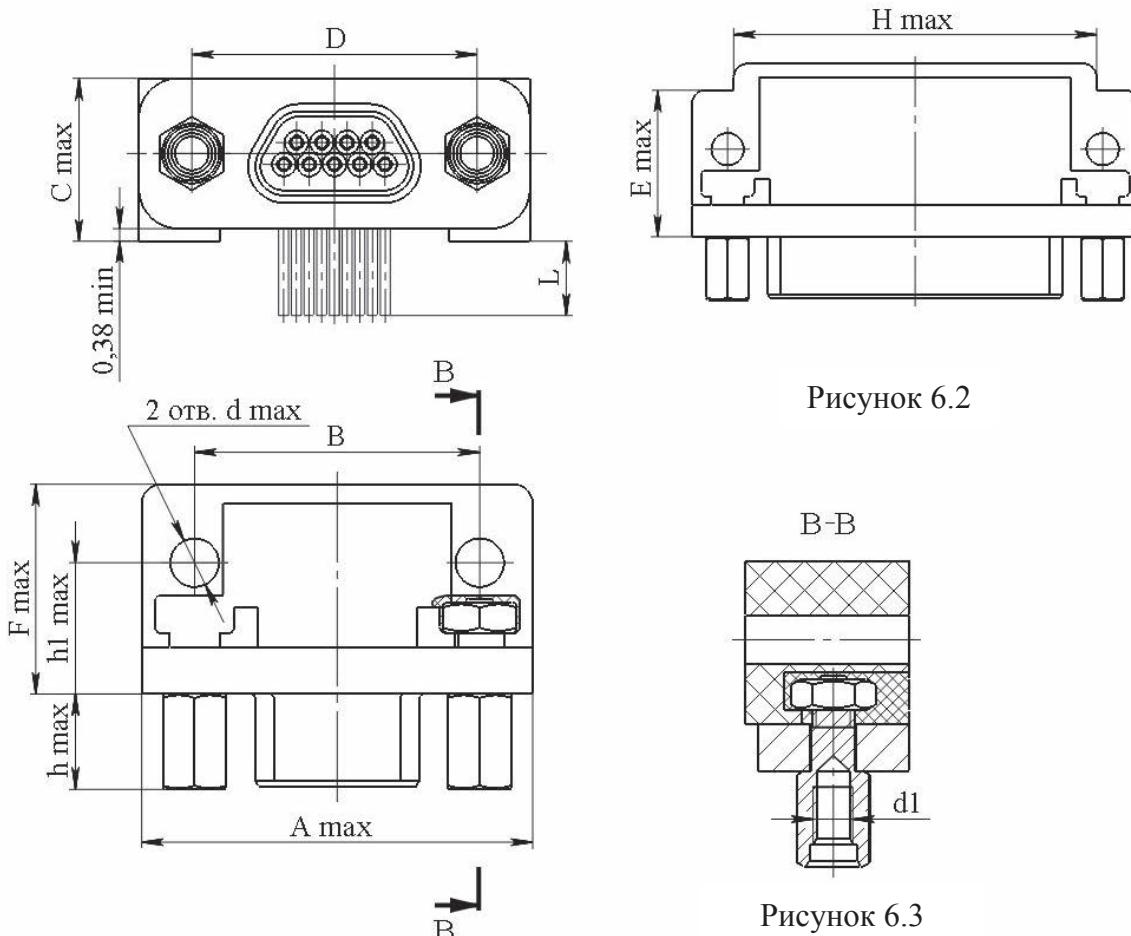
Соединитель СП397-2...Ш21...
